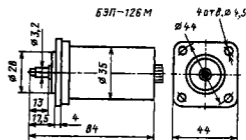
Габаритные и установочные размеры двигателей БЭП-126М, ДБ-4
